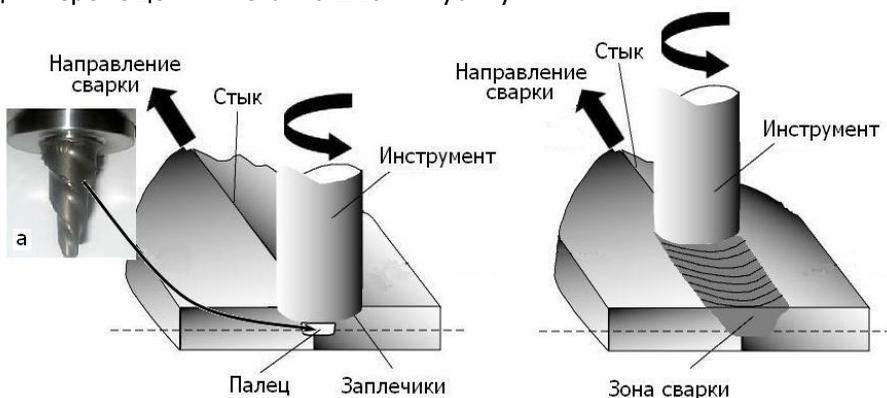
Схема процесса сварки трением с перемешиванием.
